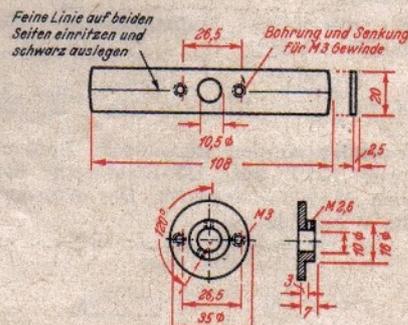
Plexiglaszeiger und zugehöriger Befestigungsflansch
